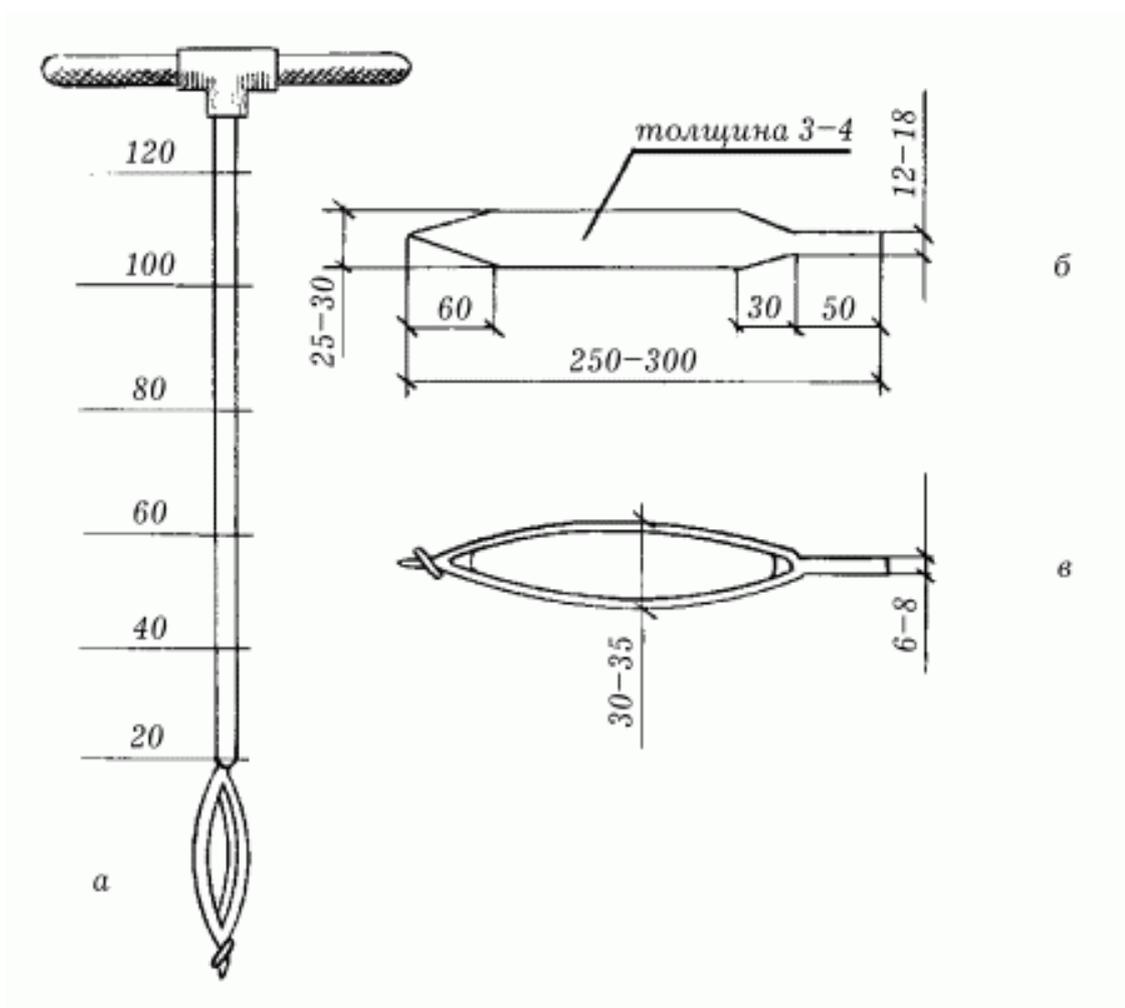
Почвенный бур: *а*– общий вид (в см); *б*– заготовка; *в* – головка бура.
